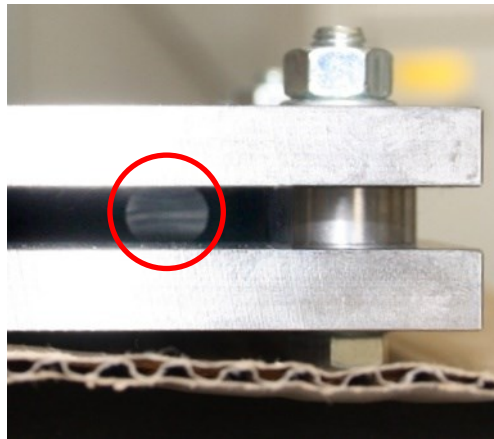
verpresste O-Ring-Hälfte im Plattenpaar
